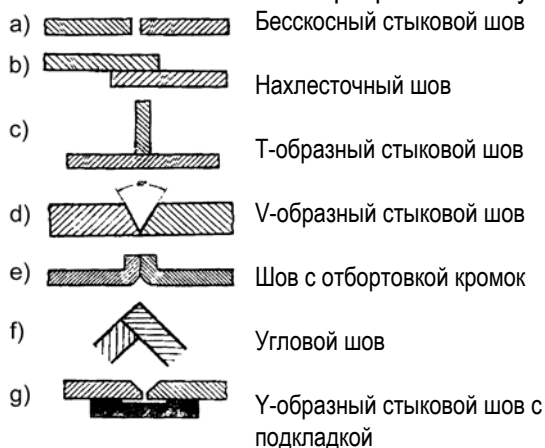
Наиболее важные формы кромок при сварке ВИГ
